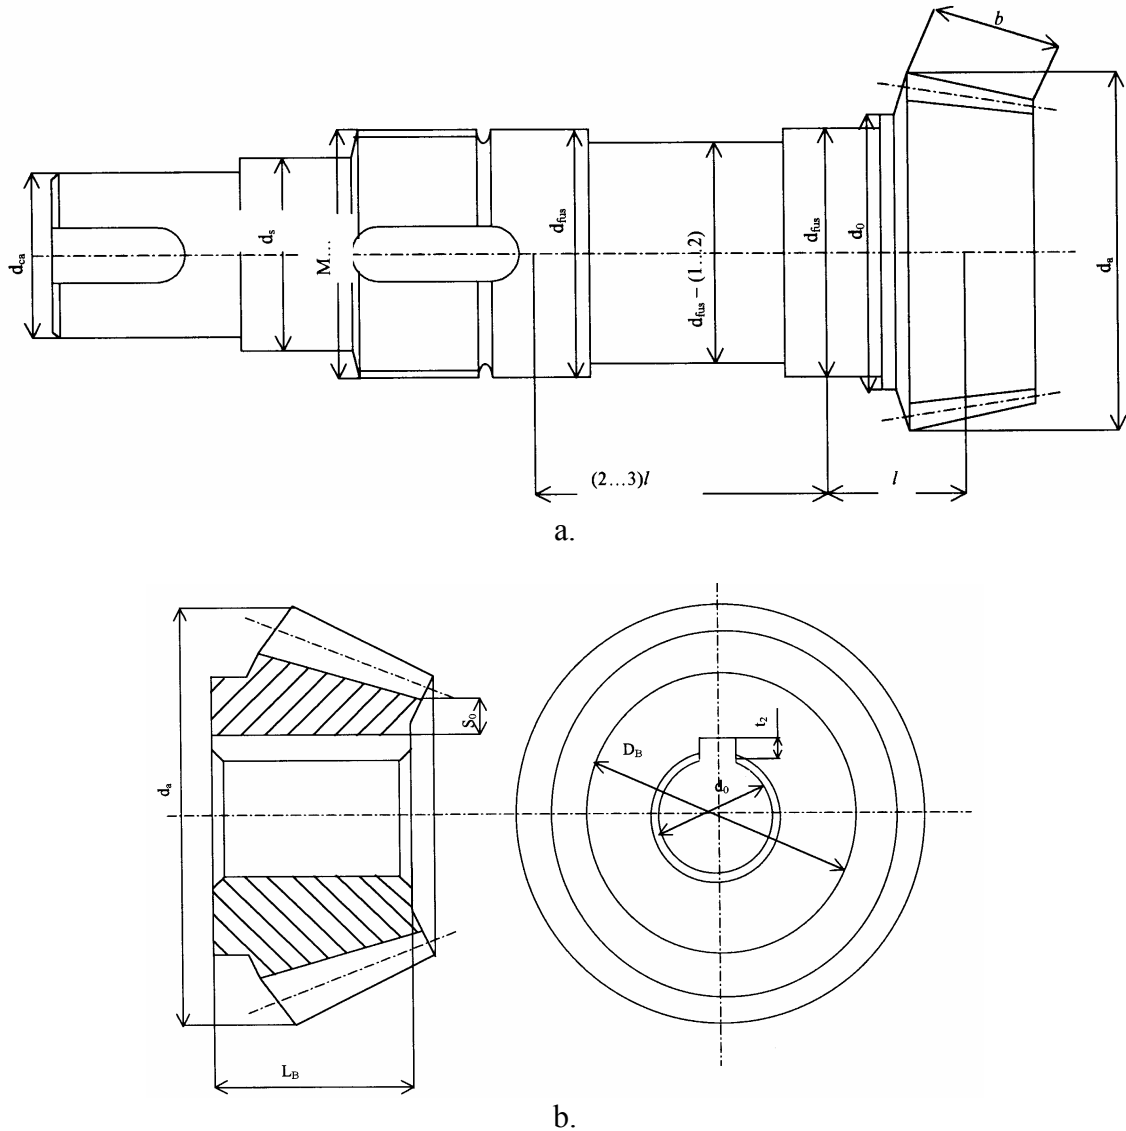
Forme constructives de pignons coniques (arbre/pignon)(a) ou indépendante (b)
